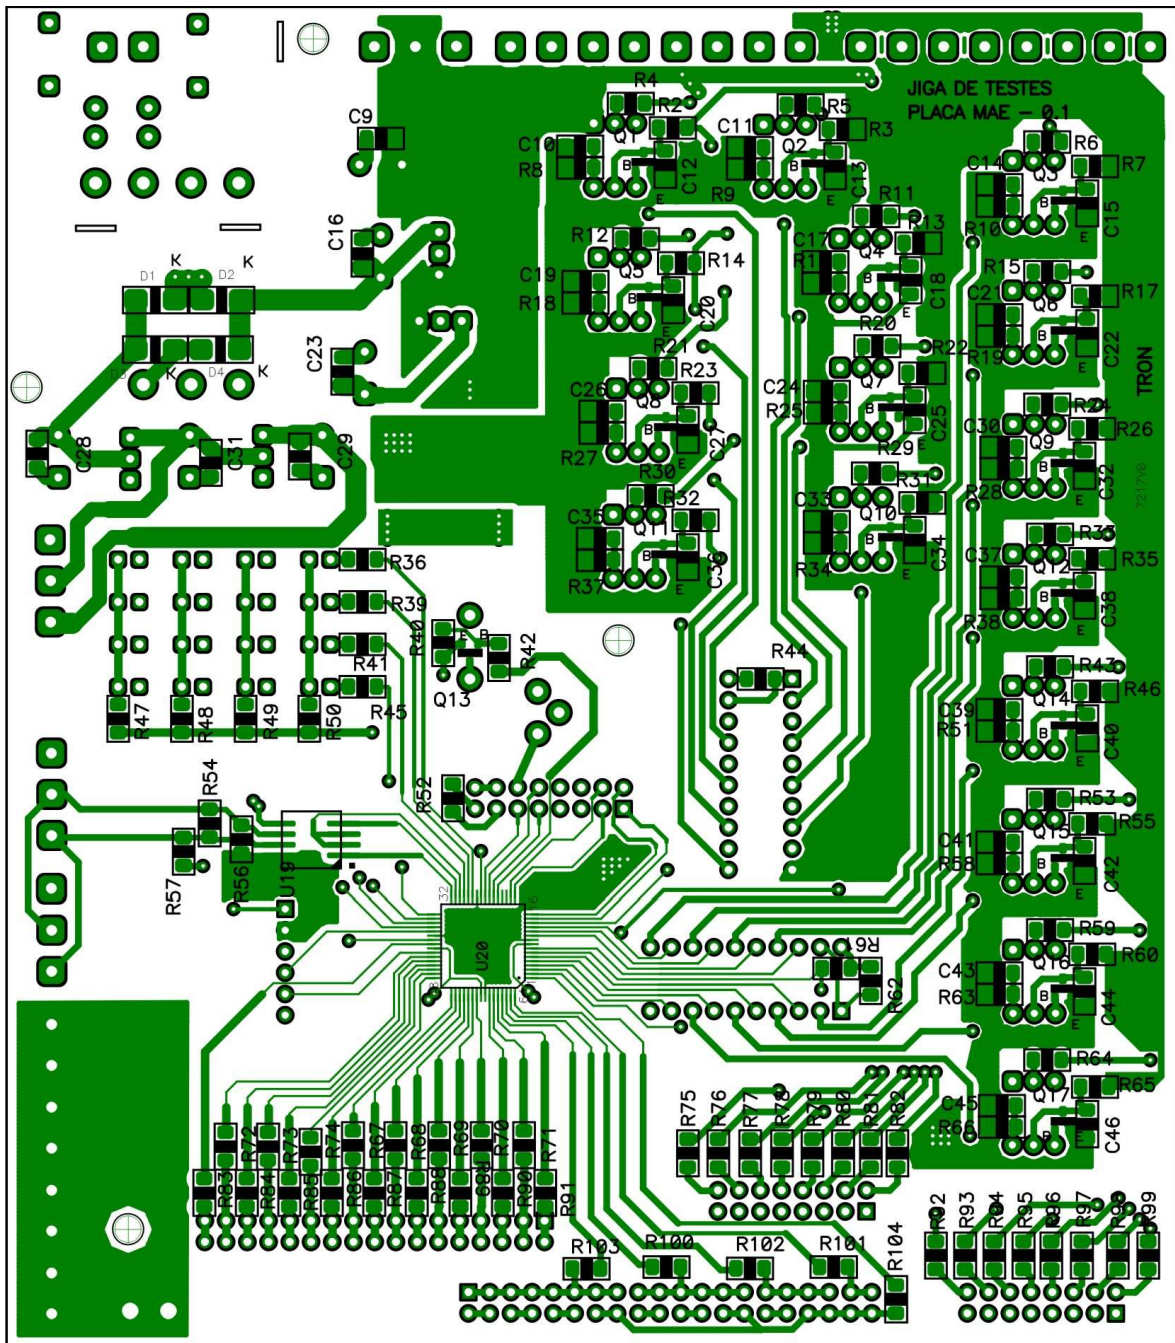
Placa Mãe - Face da Solda e dos Componentes SMD
